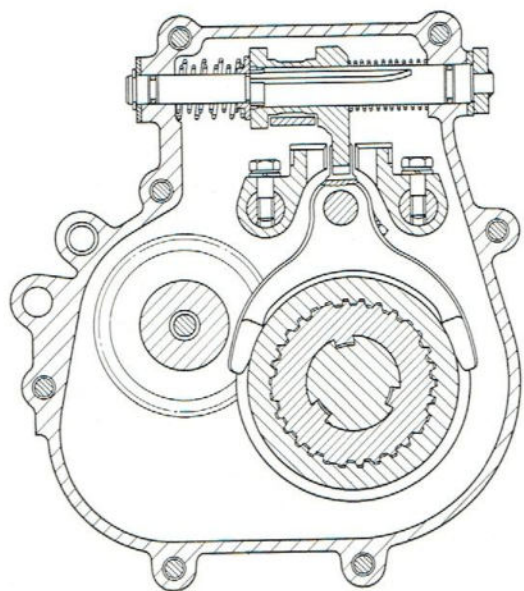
Querschnitt des Getriebes durch den inneren Schaltzwischenhebel.
